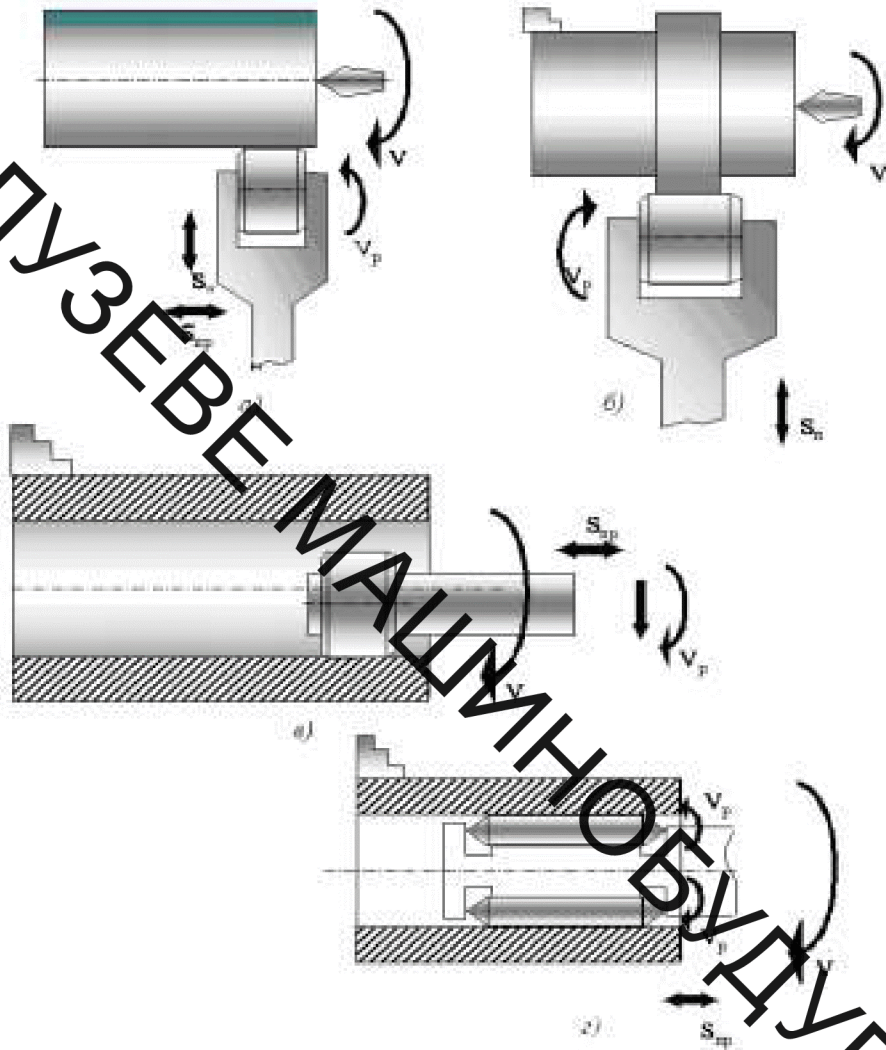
Зовнішнє обкатування та розкатування внутрішніх циліндричних поверхонь
